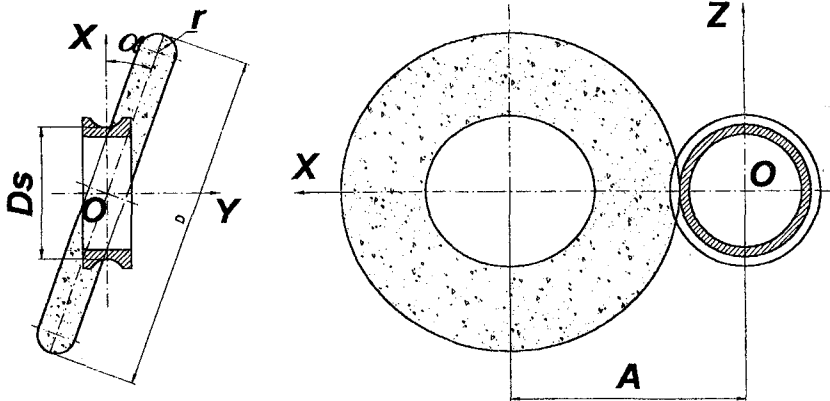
Схема способа шлифования наклонным кругом деталей типа внутренних колец подшипников
